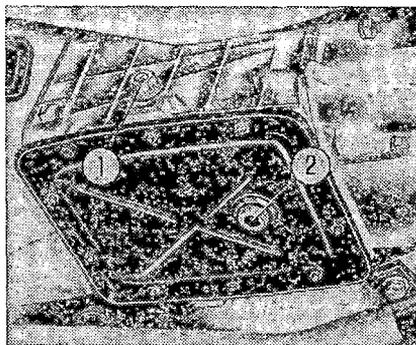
Пробки наливного (контрольного) и сливного отверстий в коробке передач
